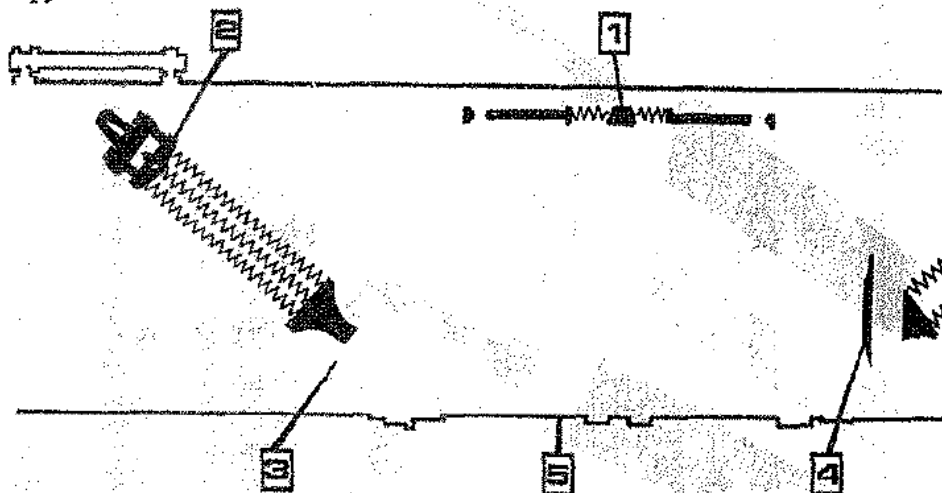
Схема вида жатки сзади (вид сзади): 1 – растяжки; 2 – блоки пружин; 3 – механизм подвески певый; 4 – боковые щитки; 5 – переходной щиток
